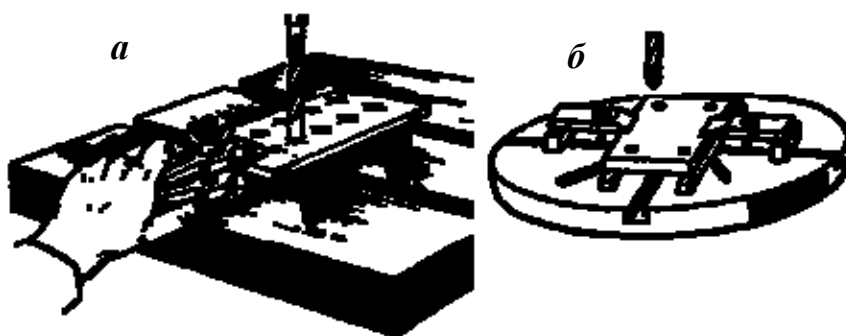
Некоторые способы крепления деталей при сверлении:
